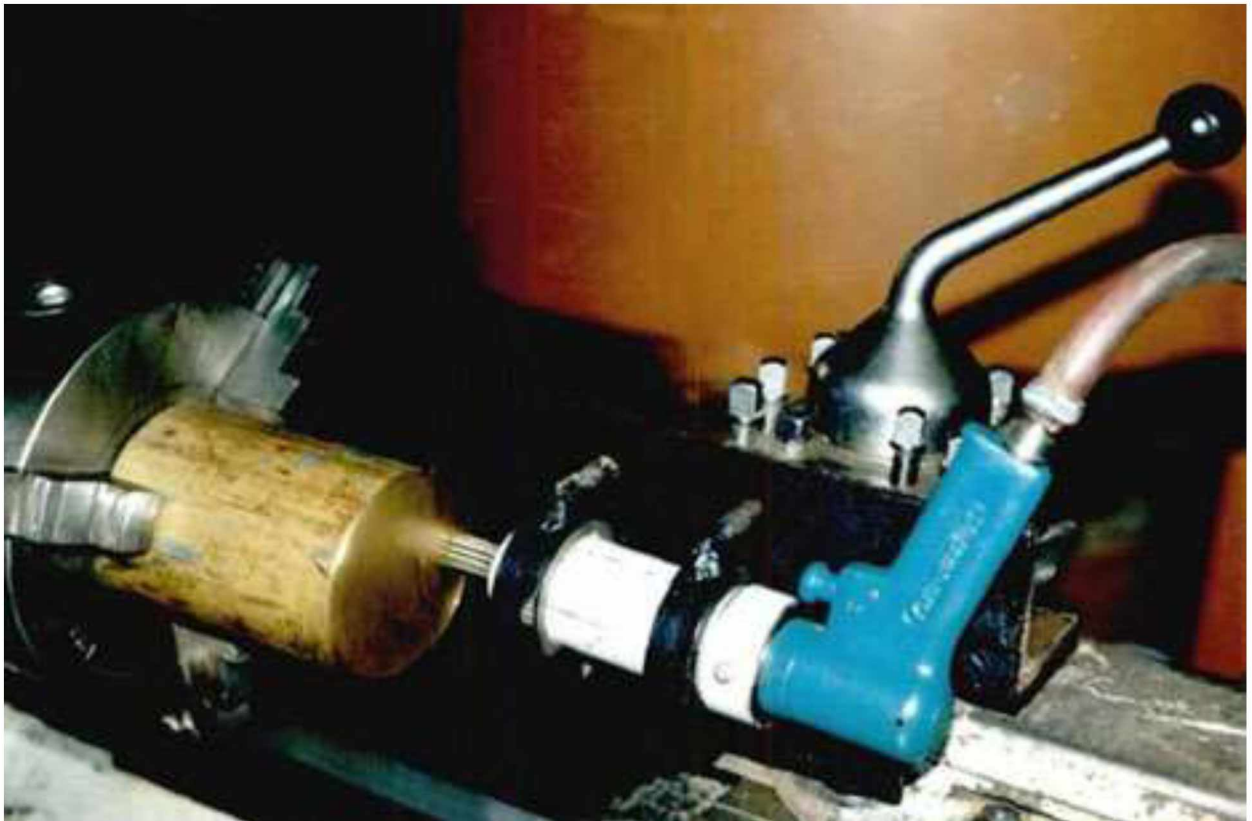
Обладнання для нанесення регулярних мікрорельєфів на поверхнях тіл обертання із використанням верстатів токарної групи
